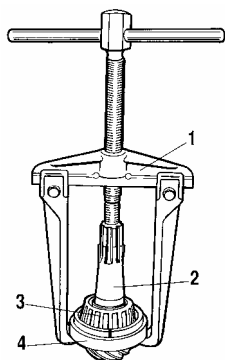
Снятие внутреннего кольца заднего подшипника ведущей шестерни универсальным съемником А.40005/1/7:
